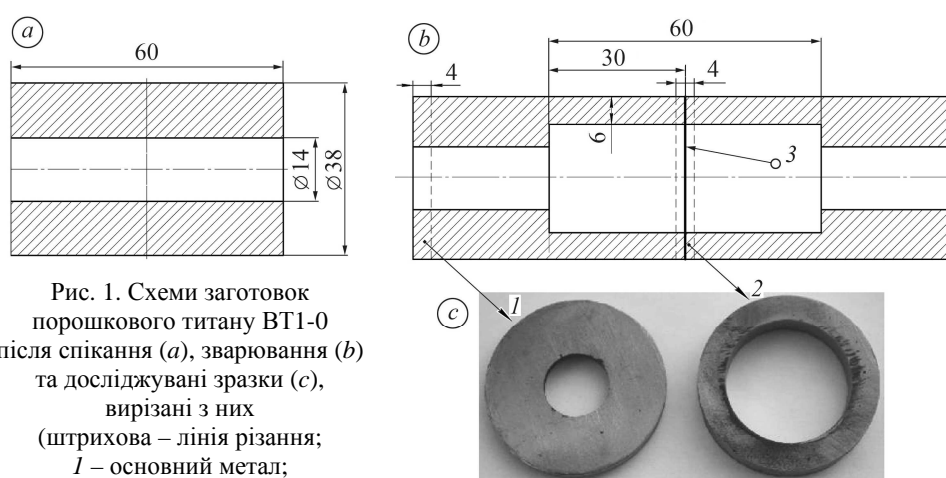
Схеми заготовок порошкового титану ВТ1-0 після спікання (а), зварювання (б) та досліджувані зразки (с), вирізані з них (штрихова – лінія різання; 1 – основний метал; 2 – зона шва та термомеханічного впливу; 3 – зварний шов).
